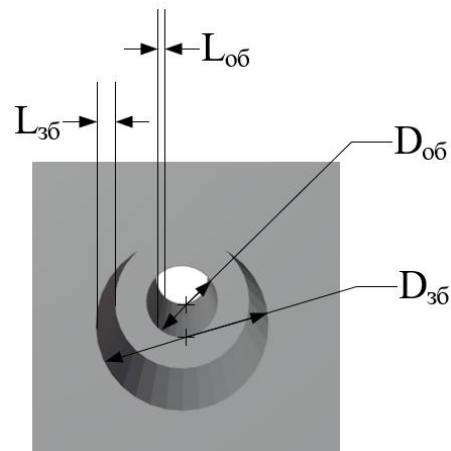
Частина моделі для 3D-друку блоку з'єднання – заглиблення з отвором для болта блоку з'єднання
